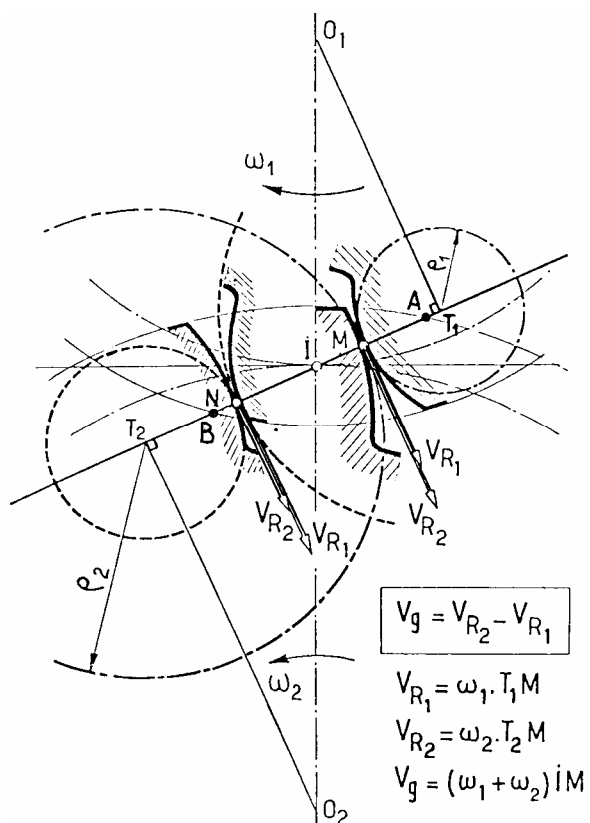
Contacto entre as faces dos dentes de uma engrenagem [8].
